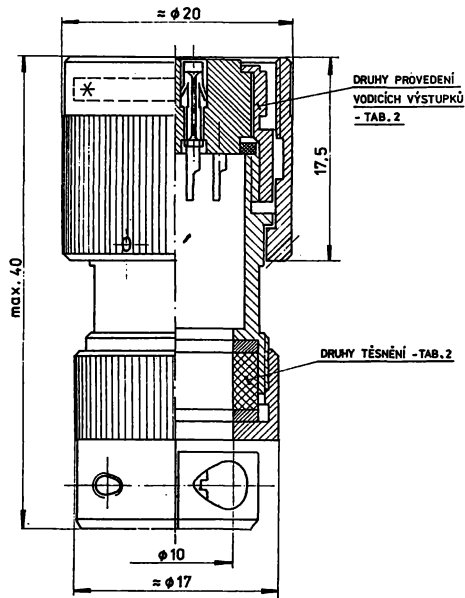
7pólová kabelová zásuvka WK 180 36
